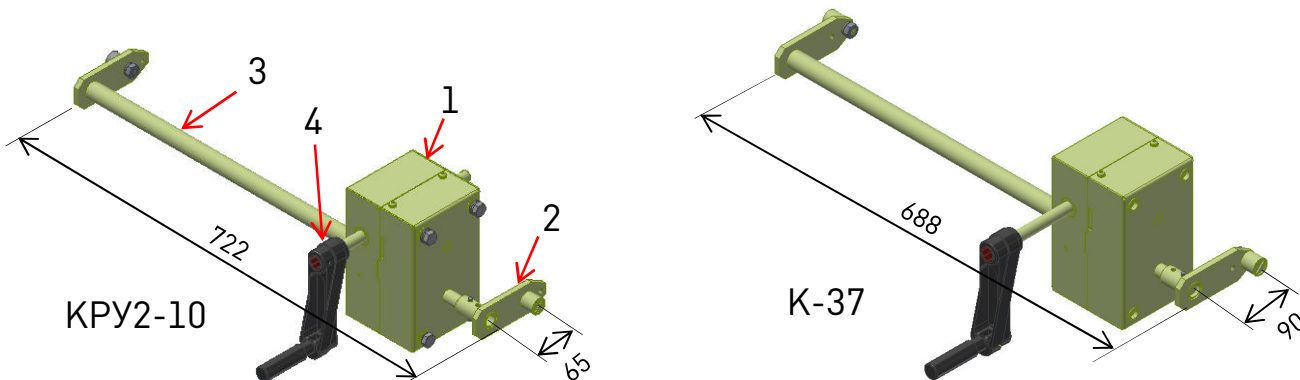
Схема узла блокировки и редукции ВЭ КРУ2-10 и К-37.
